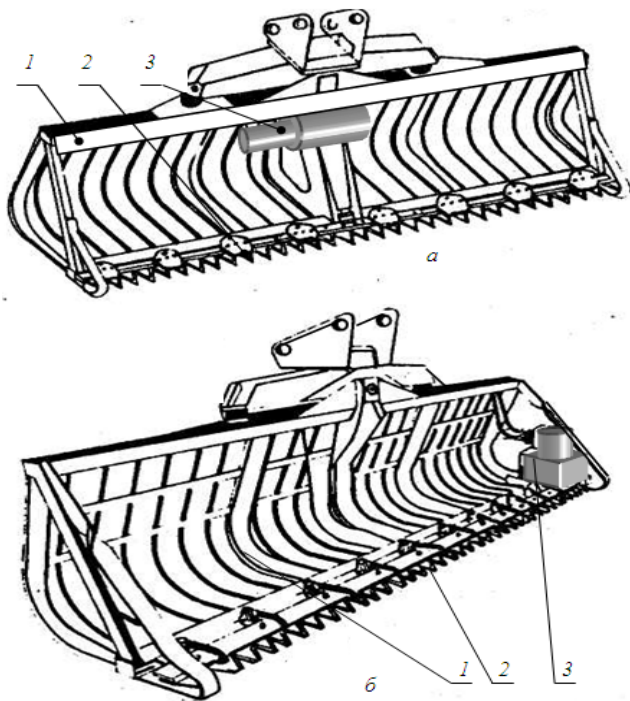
Рабочий орган ковша-косилки: *а* – с центральным расположением привода; *б* – с боковым; 1 – ковш; 2 – режущий аппарат; 3 – гидромотор с редуктором
